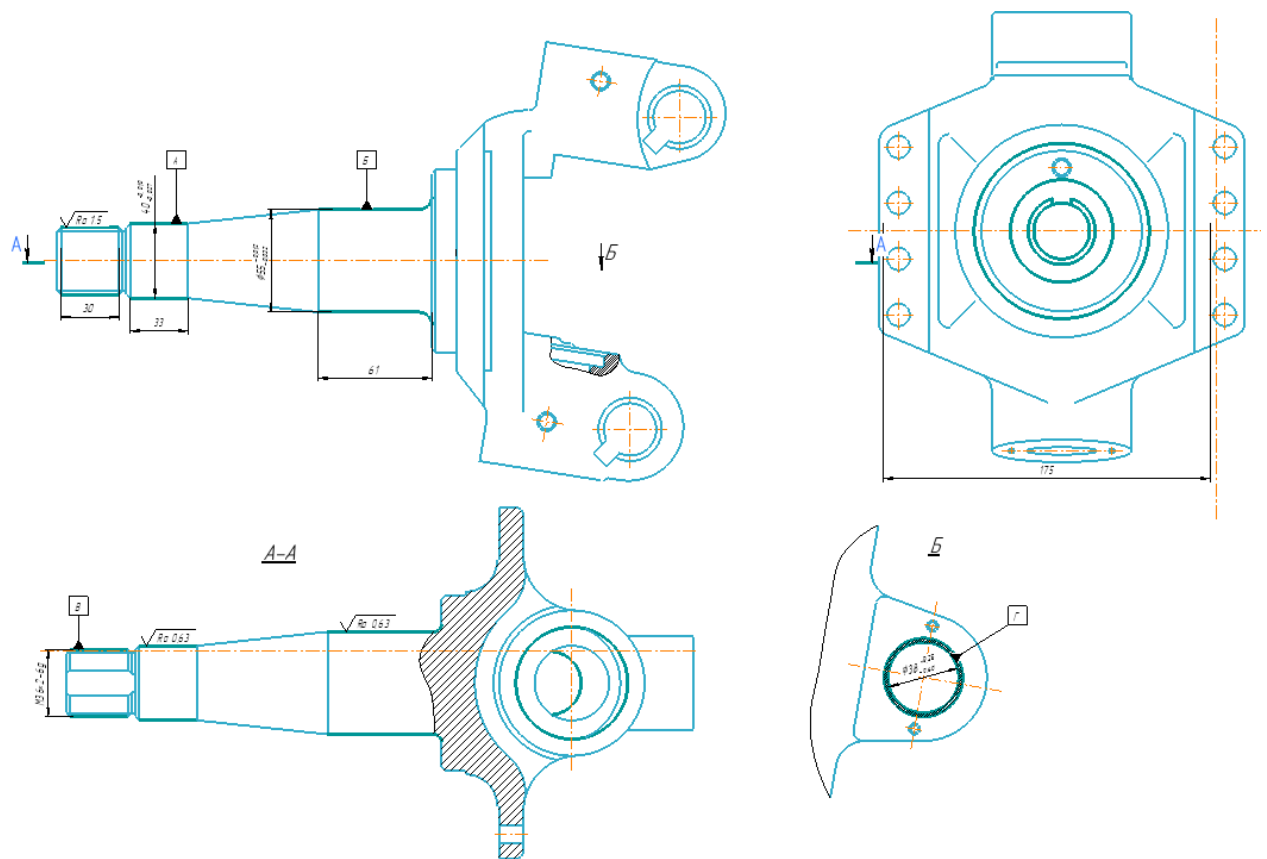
Поворотний кулак передньої підвіски автомобіля ЗіЛ-131
